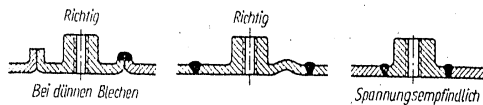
Schweißverbindungen, falsch und richtig
